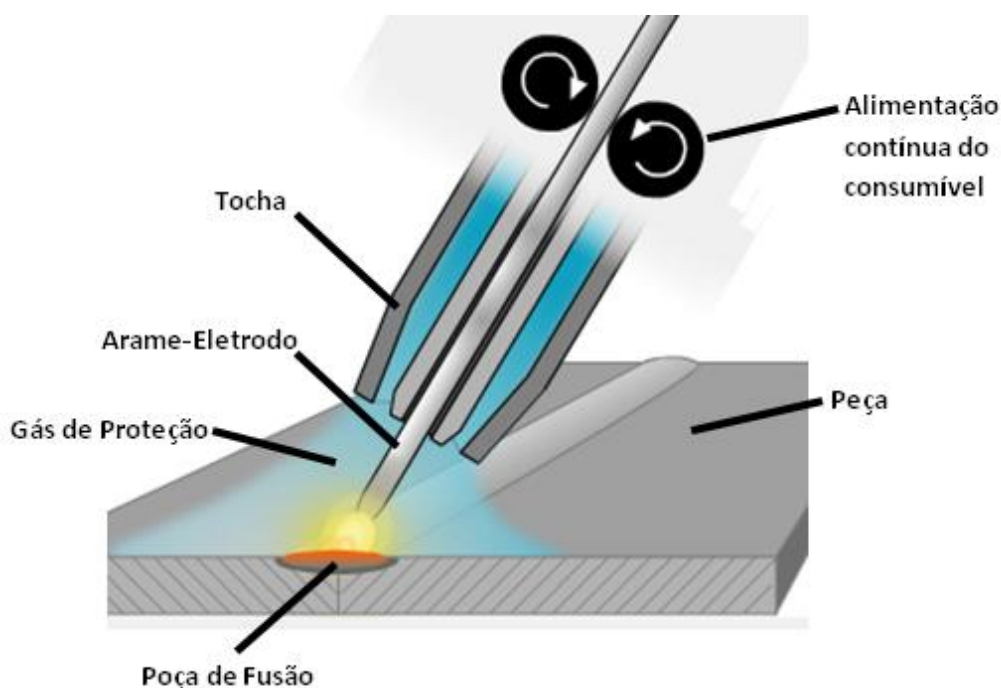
Esquema representativo da soldagem MIG/MAG [Adaptado de ESAB, 2012].
